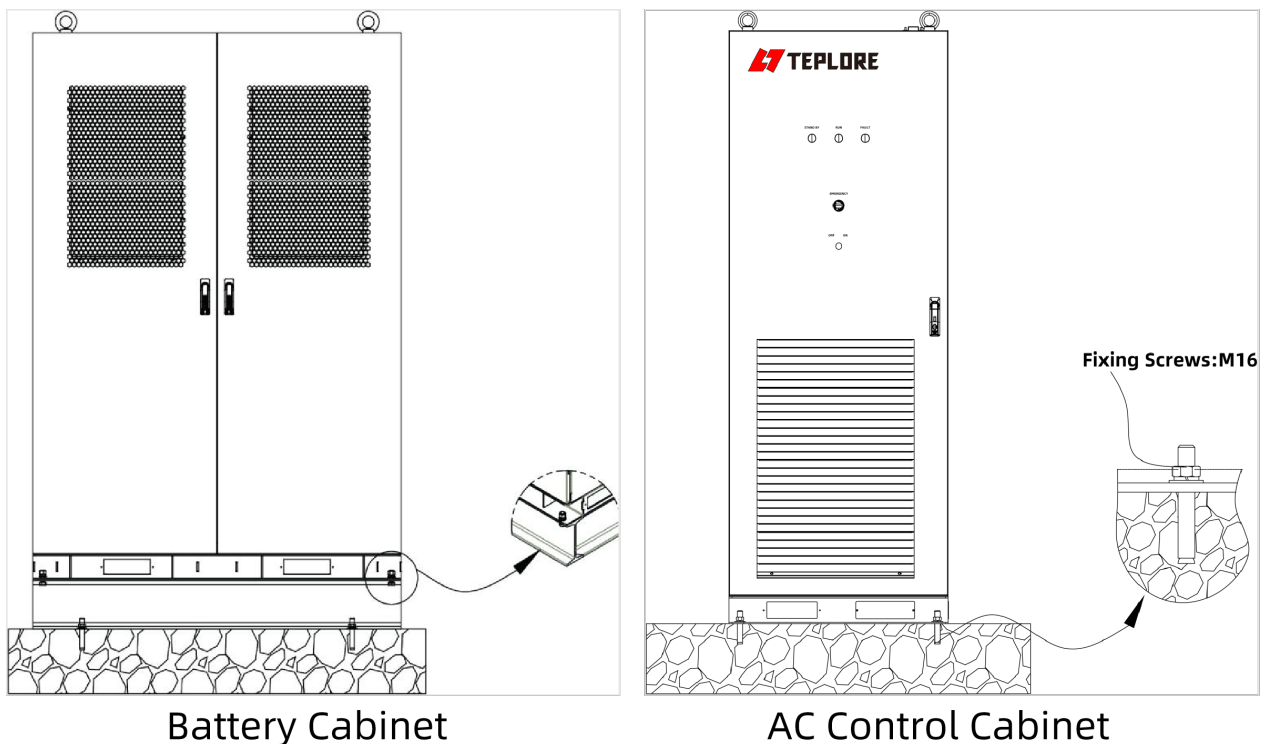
Schrauben Sie die Gehäuse zusammen
